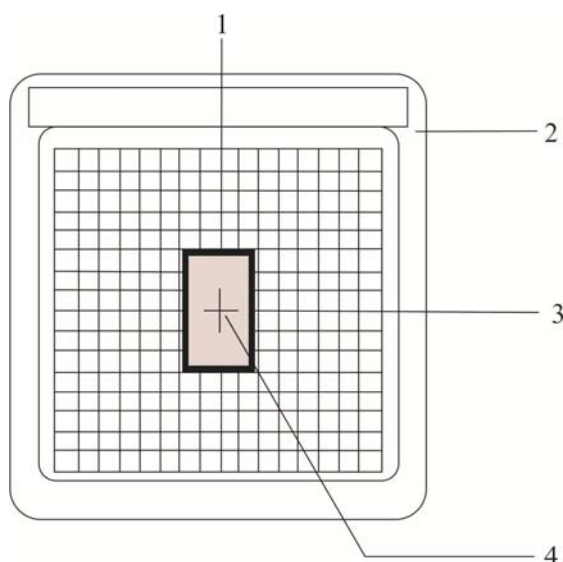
Место для установки заготовки: 1 — центральная вертикальная линия; 2 — стол; 3 — центральная горизонтальная линия; 4 — центр заготовки.
